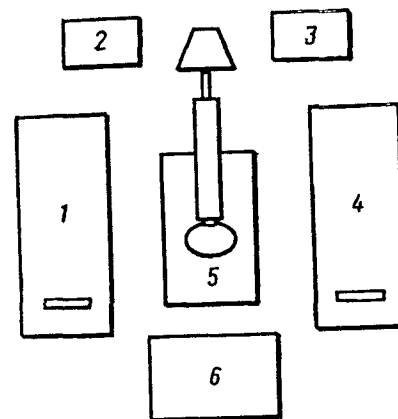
Размещение оборудования при обслуживании роботом двух токарных станков с ЧПУ: 1 — станок 1к 62ПУ № 1; 2 — накопитель заготовок; 3 — тара готовых изделий; 4 — станок 1К 62ПУ № 2; 5 — манипулятор робота; 6 — блок управления роботом
